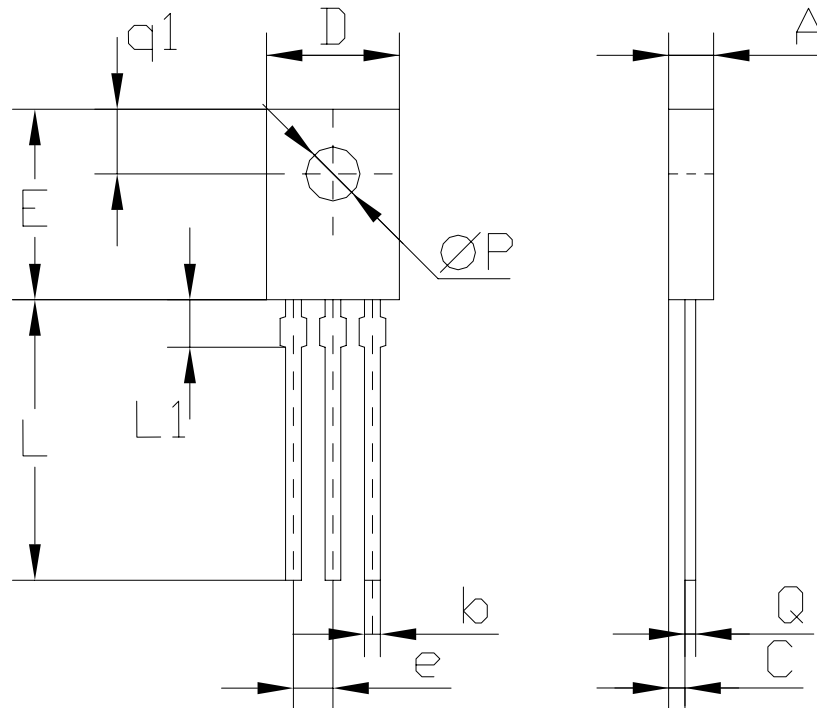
Габаритный чертеж корпуса КТ-89 (DPAK)
